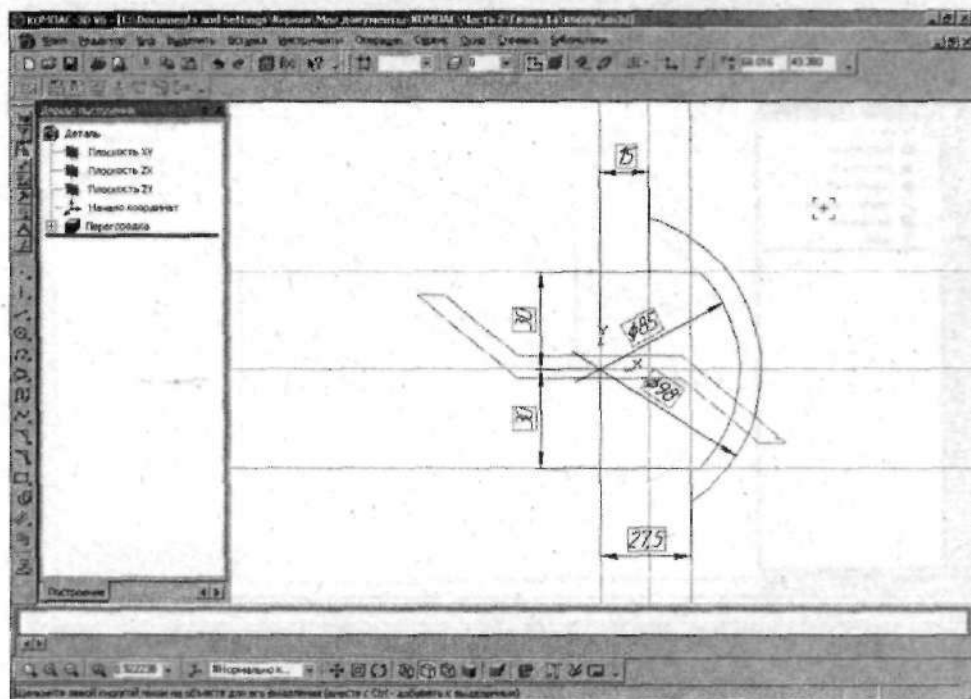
Эскиз распределительного резервуара Корпуса
